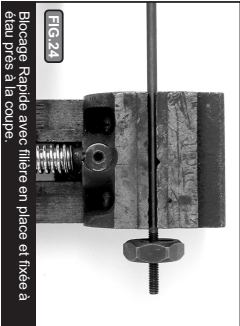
Blocage Rapide avec filière en place et fixée à l'étau près de la coupe
